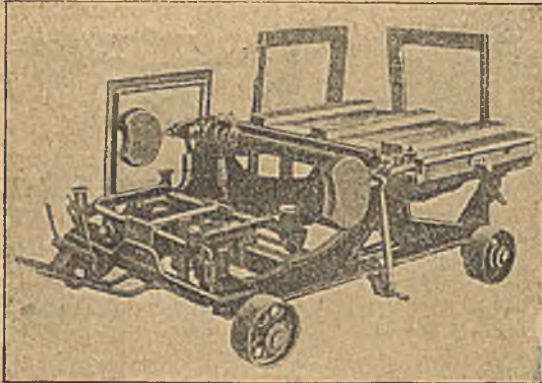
Kippbare Handdurchzieh-Formmaschine für Ofenplatten und Rahmen.
